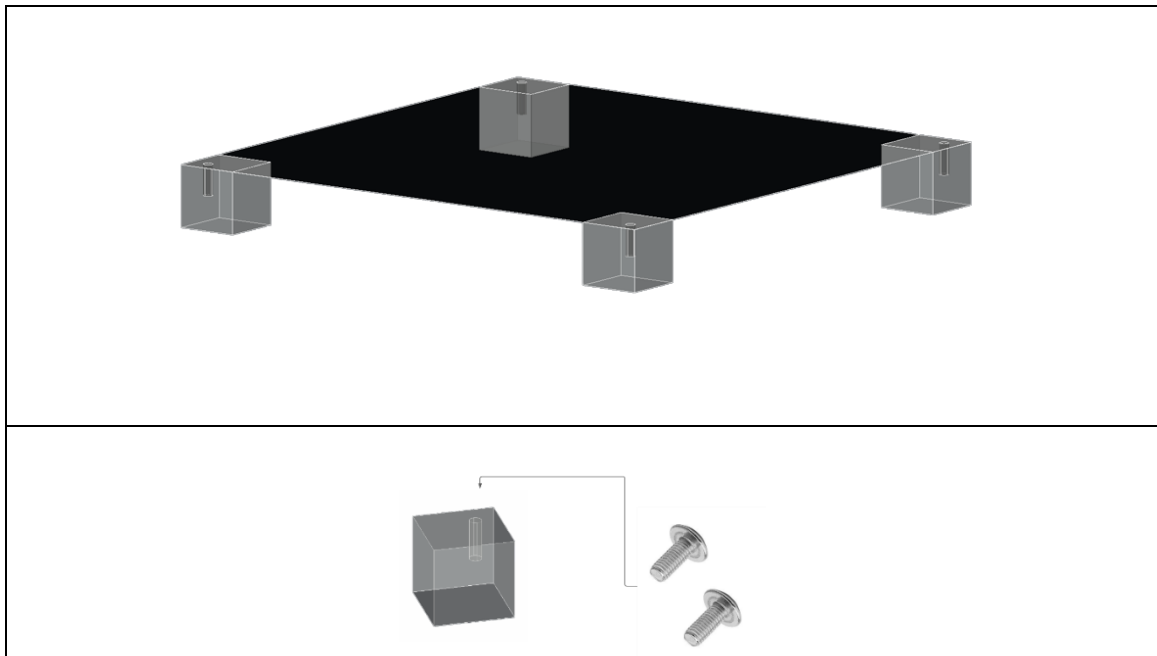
Modelado en 3D de la parte inferior de la carcasa.
